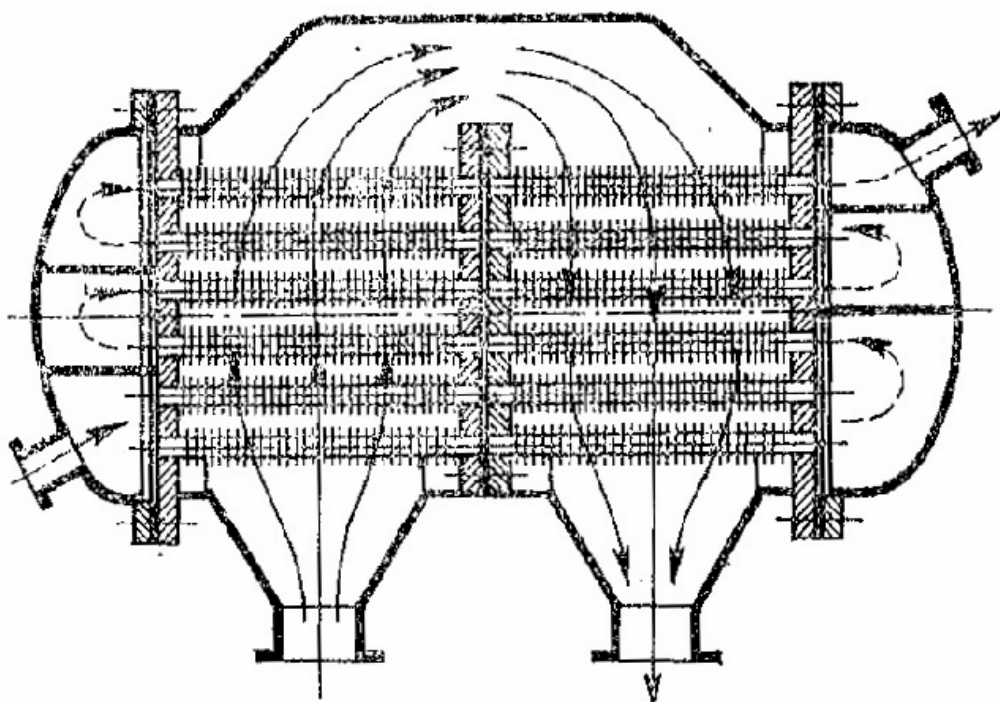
Принцип устройства кожухотрубного газоохладителя.
